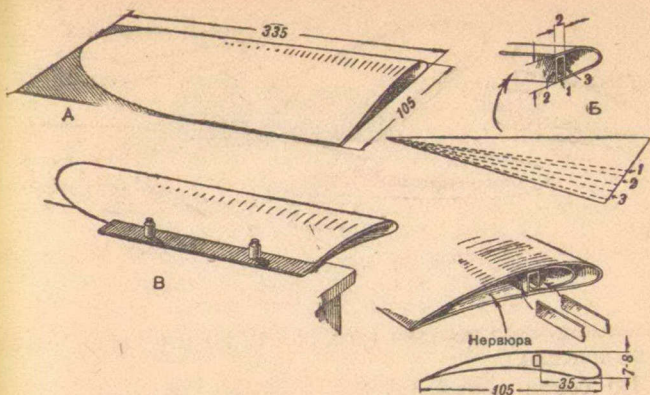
Изготовление крыла: А—крыло и его размеры, Б—лонжерон, В—изготовление консоли.
